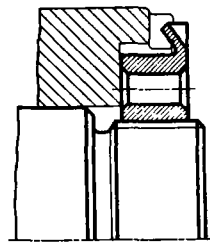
Стопорение кольцевой гайки отгибом фланца гайки в паз
